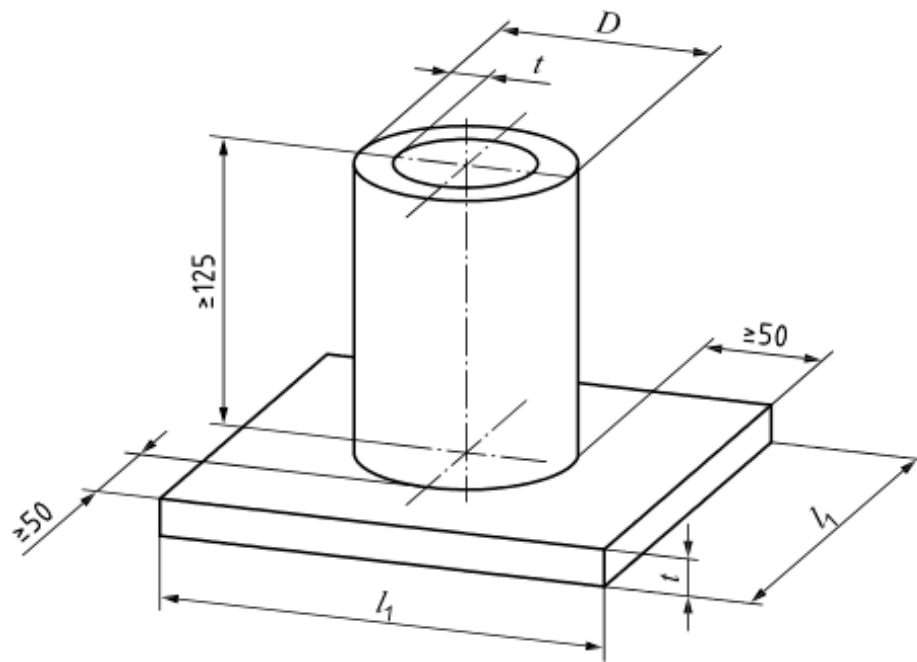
Розміри труб та пластин для експертизи зварювання на зварних з'єднаннях труба-пластина.
